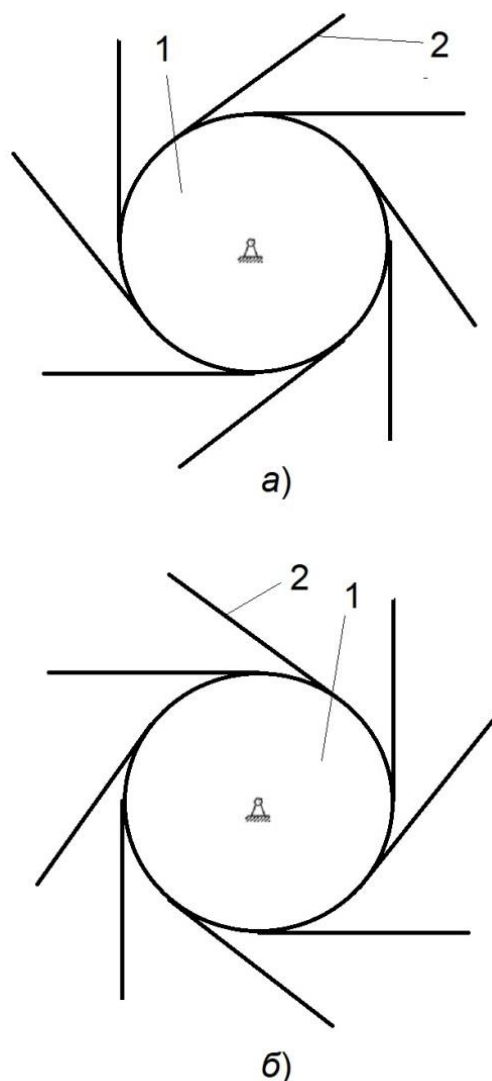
Условная схема сечения смесительного барабана с упругими лопатками в различных ярусах: а – ярус А; б – ярус В; 1 – цилиндрический барабан; 2 – лопатка
